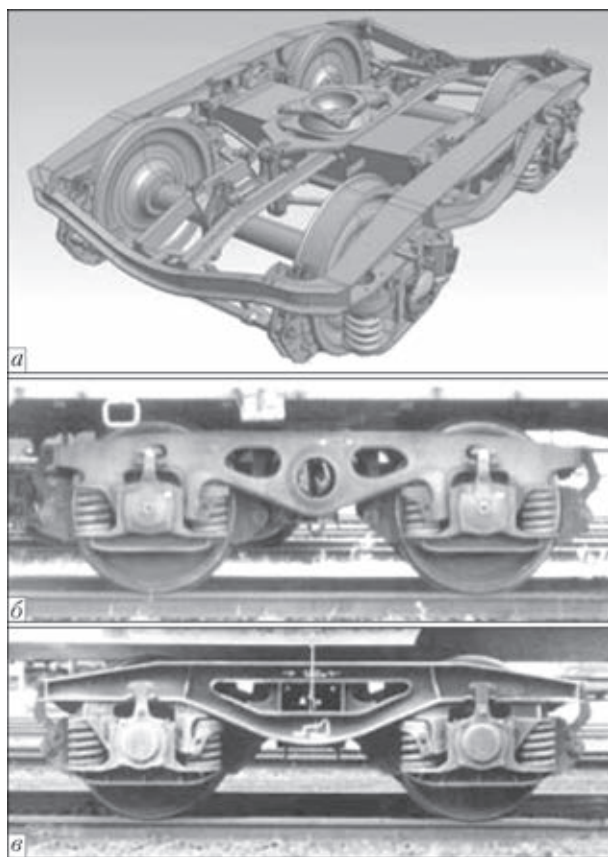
Общий вид конструкции тележки Y25 (а), литая конструкция тележки типа Y25Cm (б) и сварная конструкция тележки Y25C (в)
